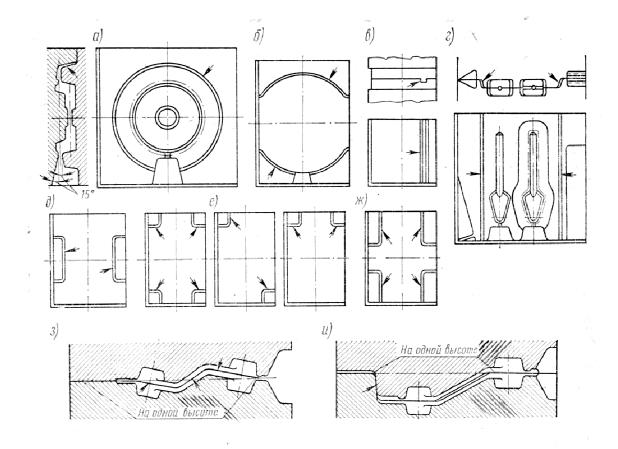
Схема замков штампов: а – кольцевой полный; б – кольцевой неполный; в – шлицевый; г – долевой; д – боковой; е – угловой; ж – крестовой; з – самоуравновешанный; и – контрзамок. Стрелками показано положение замков
